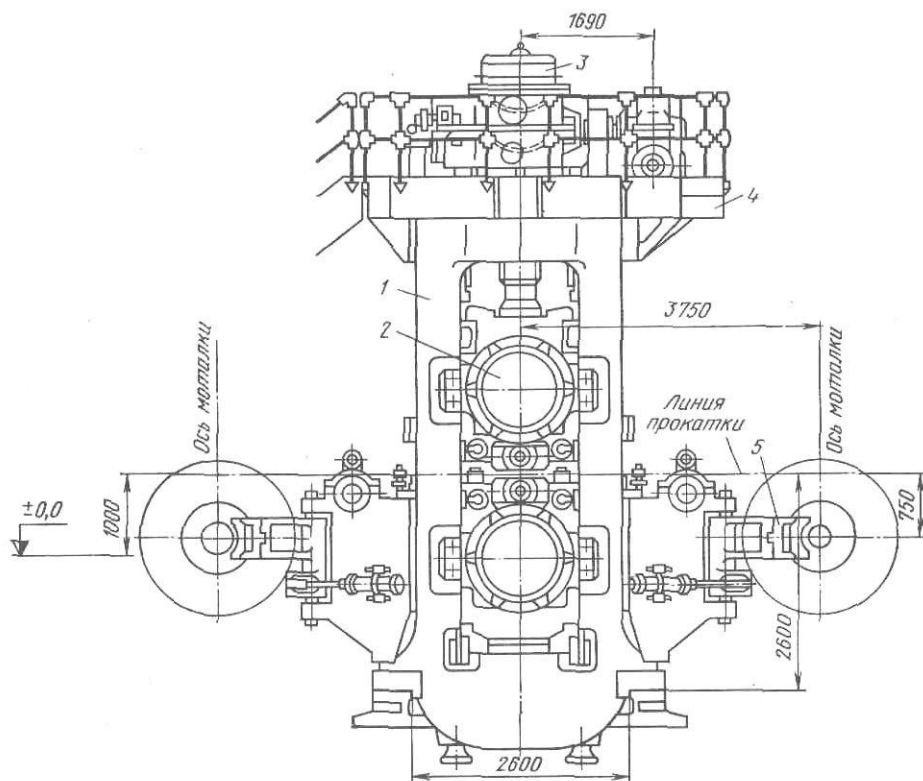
Четырехвалковая рабочая клетка 500/1300×1700 реверсивного стана холодной прокатки
